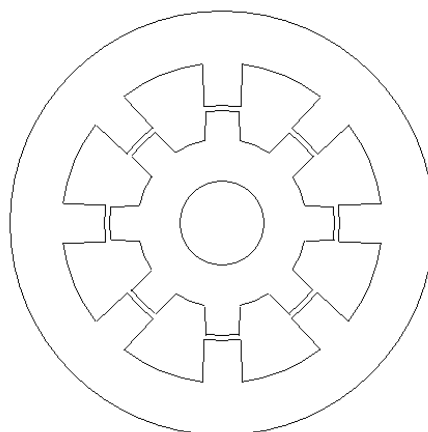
Двухфазный ВРД конструкции 8/8
